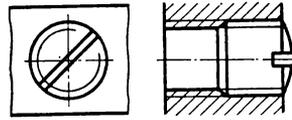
Darstellung zusammengeschrabter Gewindeteile
